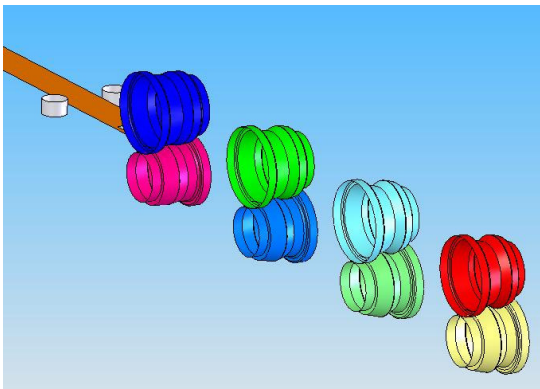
Формообразующая оснастка (4 пары роликовых калибров) для изготовления Z-образного профиля
